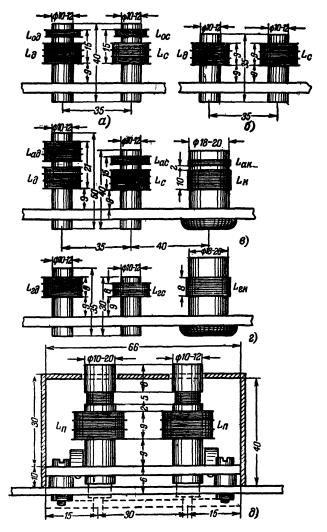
Катушки с цилиндрическими сердечниками из карбонильного железа.
